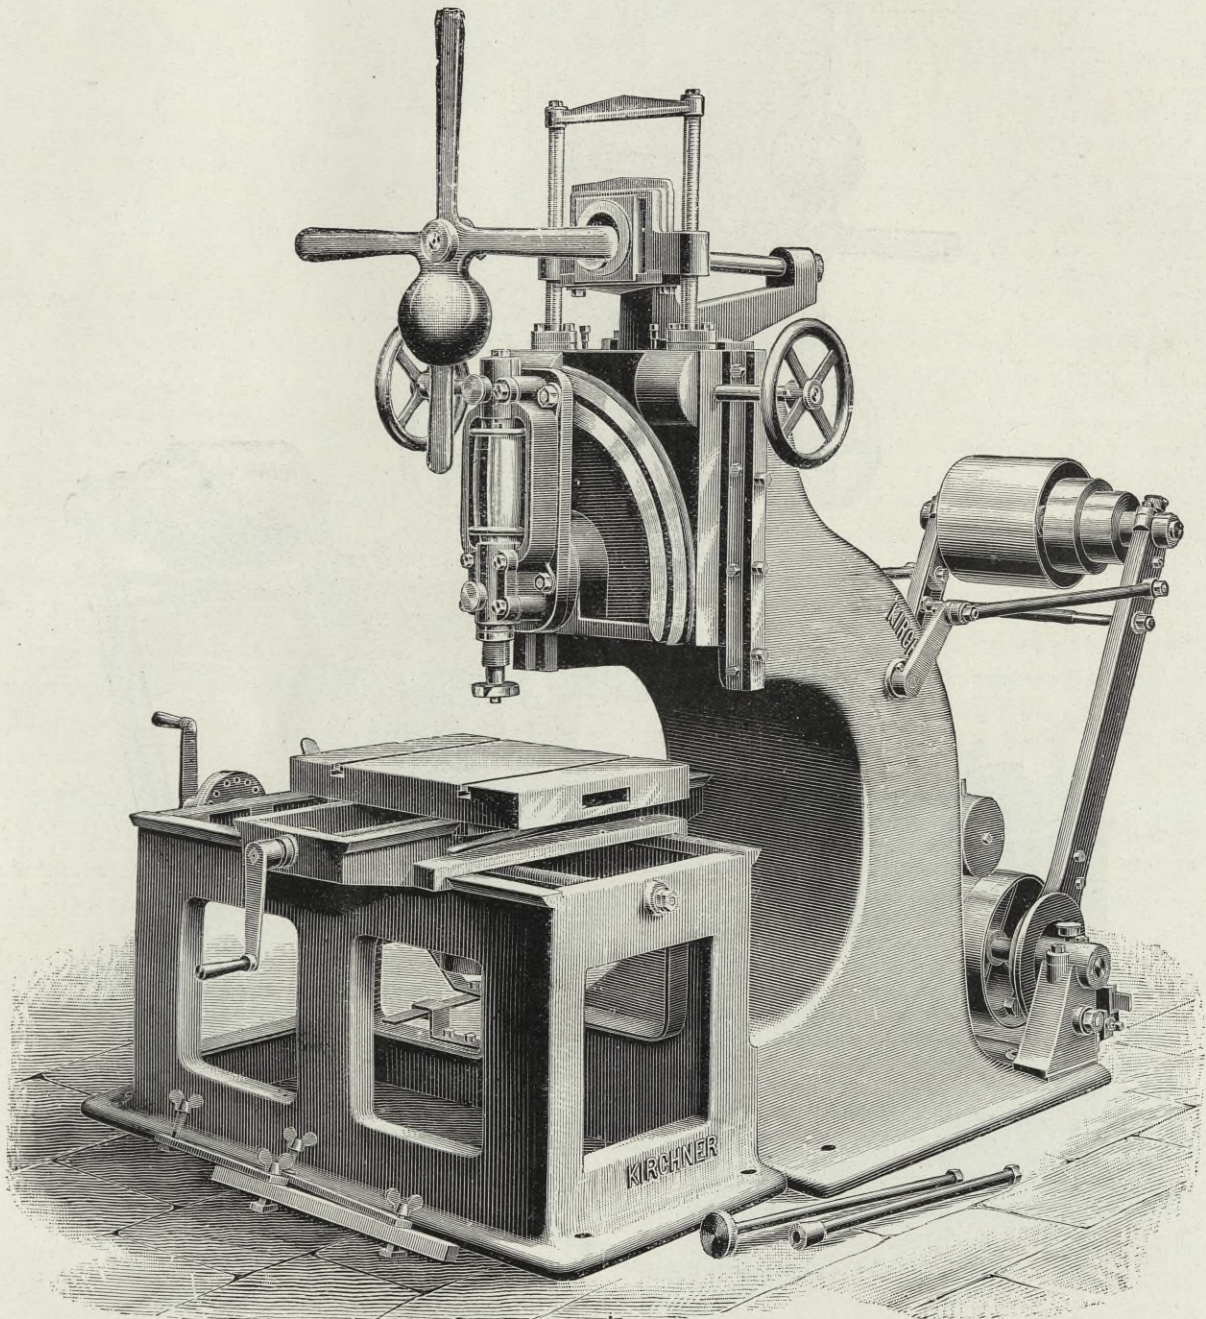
Hauptansicht der Fräsmaschine mit vertikaler Stellung der Frässpindel.
